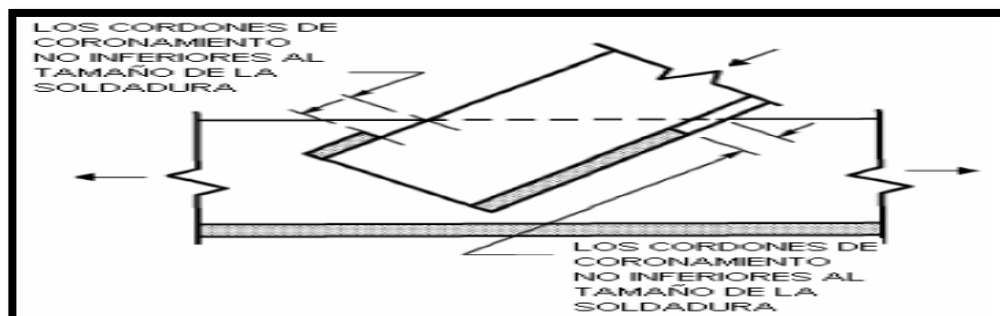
Terminación de la soldadura cerca de los bordes sujetos a tensión
